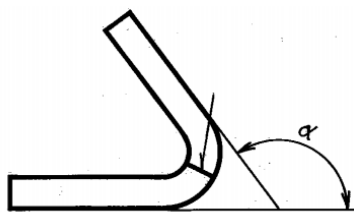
Схема випробування зварних з'єднань на згин
